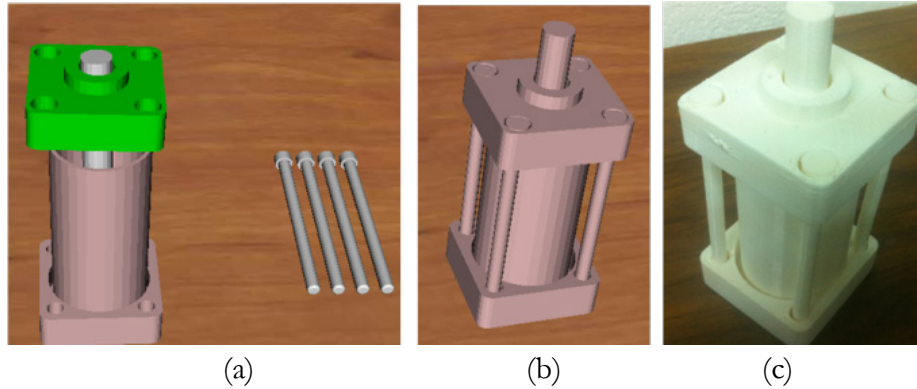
Caso de ensamble de cilindro neumático: (a) proceso de ensamble, (b) componente ensamblado, (c) prototipo rápido real.
